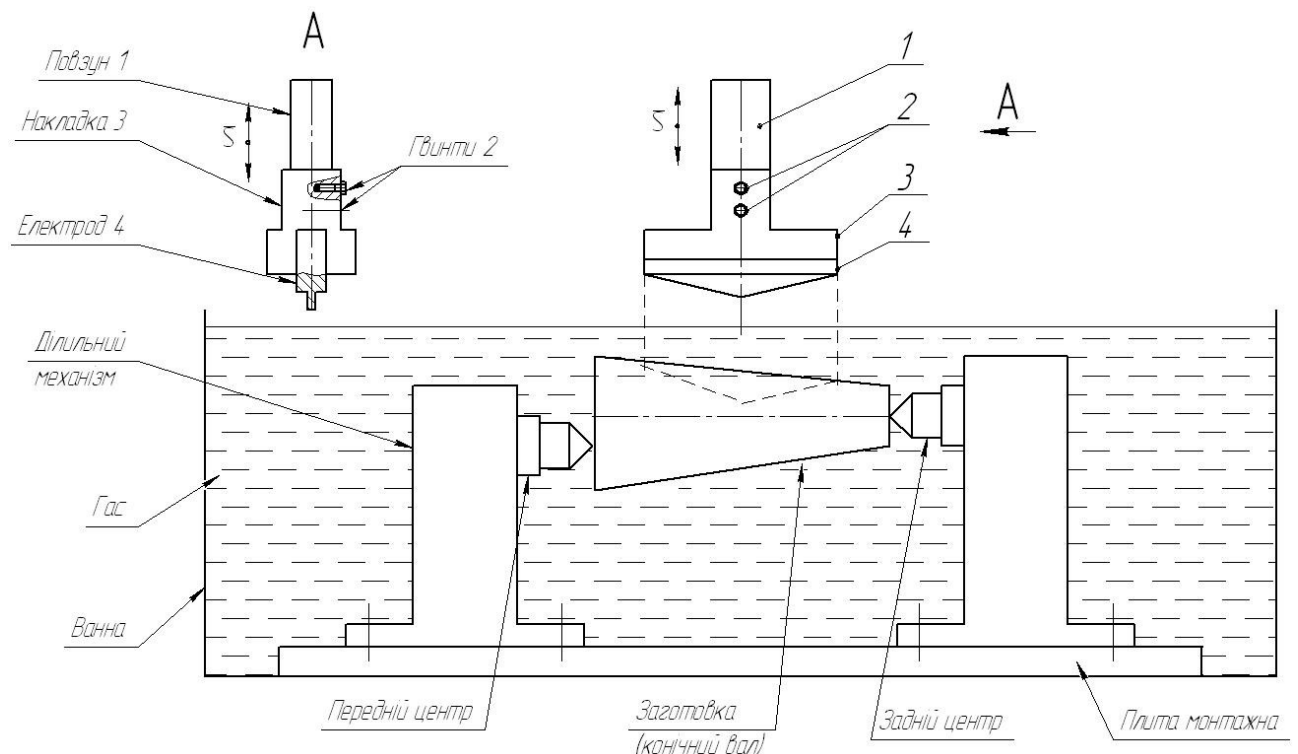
Схема нанесення канавок електроерозійним методом: 1 повзун верстата; 2 гвинти; 3 накладка; 4 електрод з латуні, який має профіль потрібної канавки; 5 монтажна плита; 6 задній центр; 7 конічна заготовка; 8 передній центр; 9 вана; 10 гас; 11 ділільний механізм.
